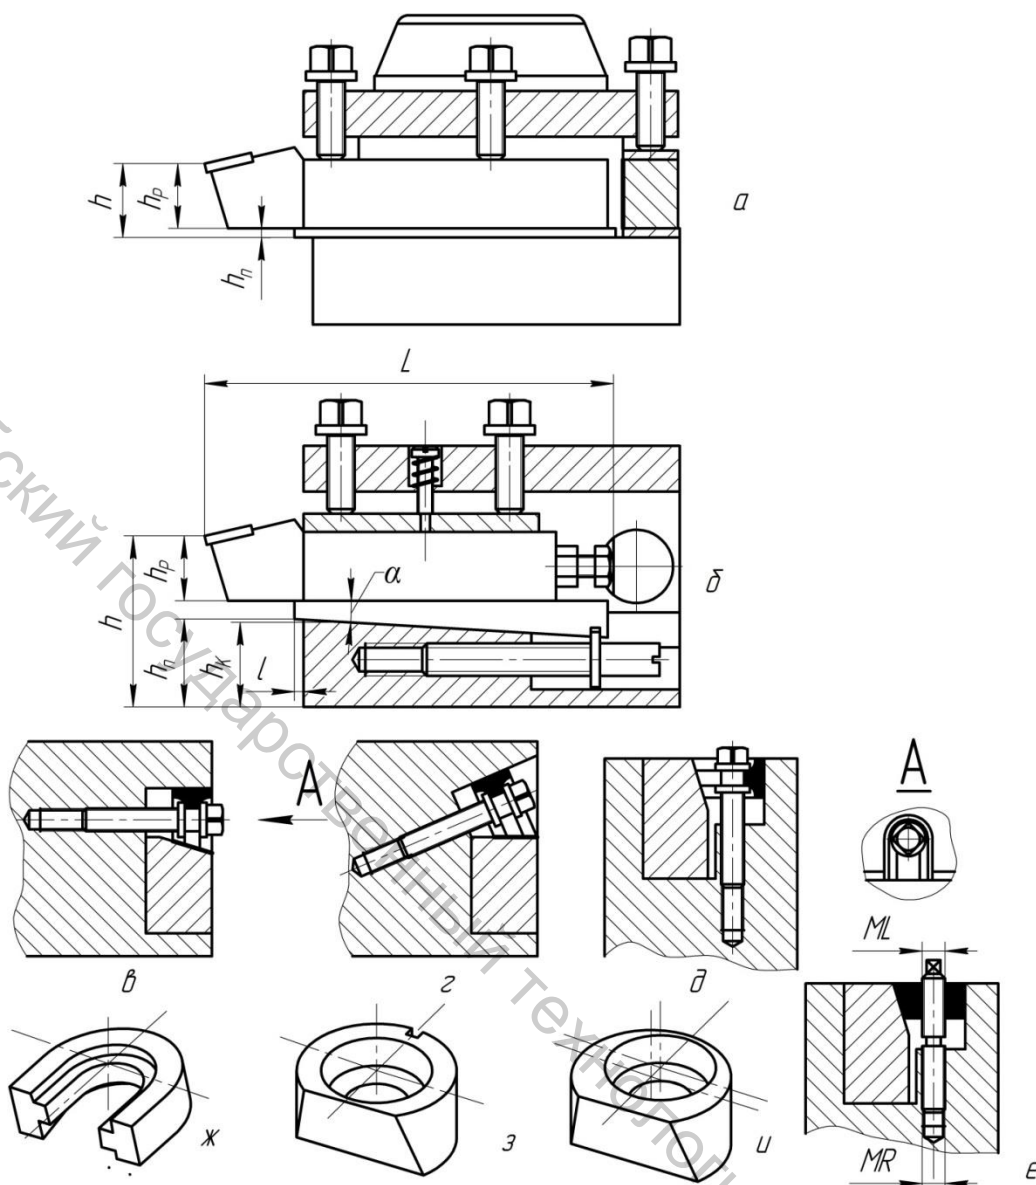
Способы крепления призматических корпусов резцов:
